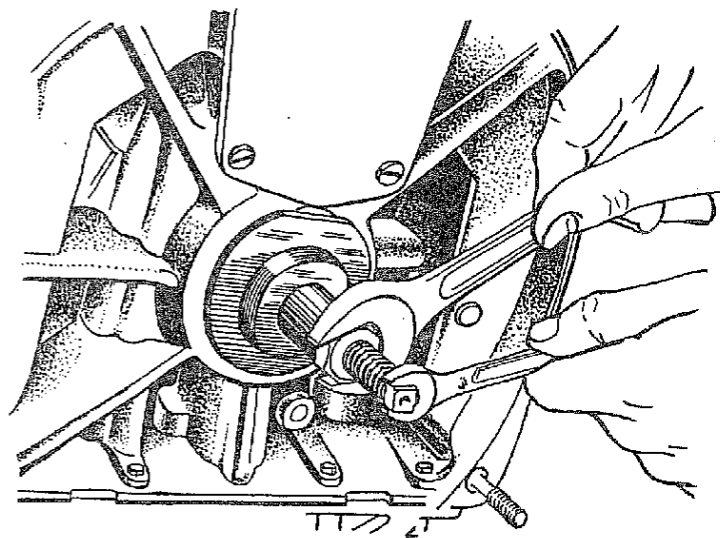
Запрессовка сальника коленчатого вала со стороны маховика
